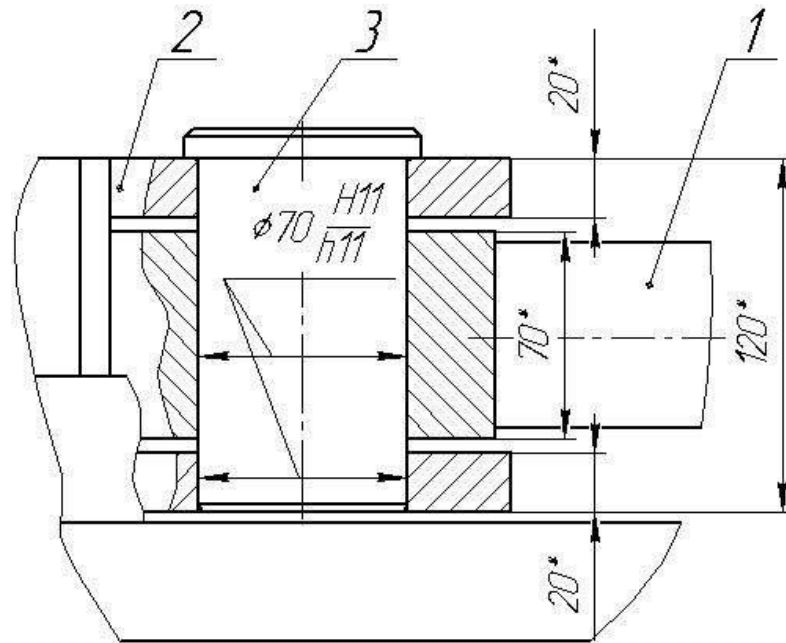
Кріплення штоку гідроциліндра до поперечини
